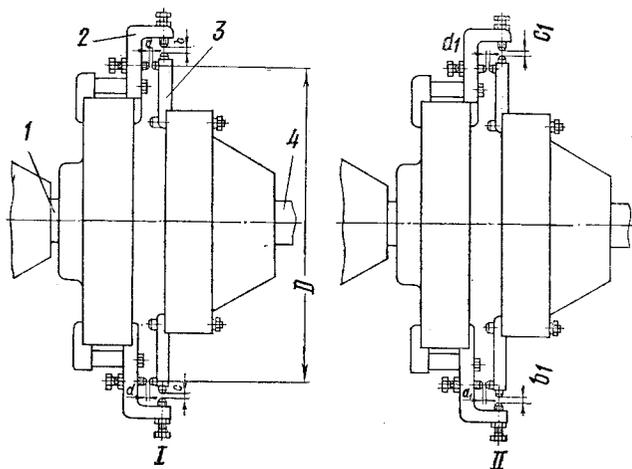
Схема установки стрел для центрирования вала дизеля с валом агрегата приводимого:
